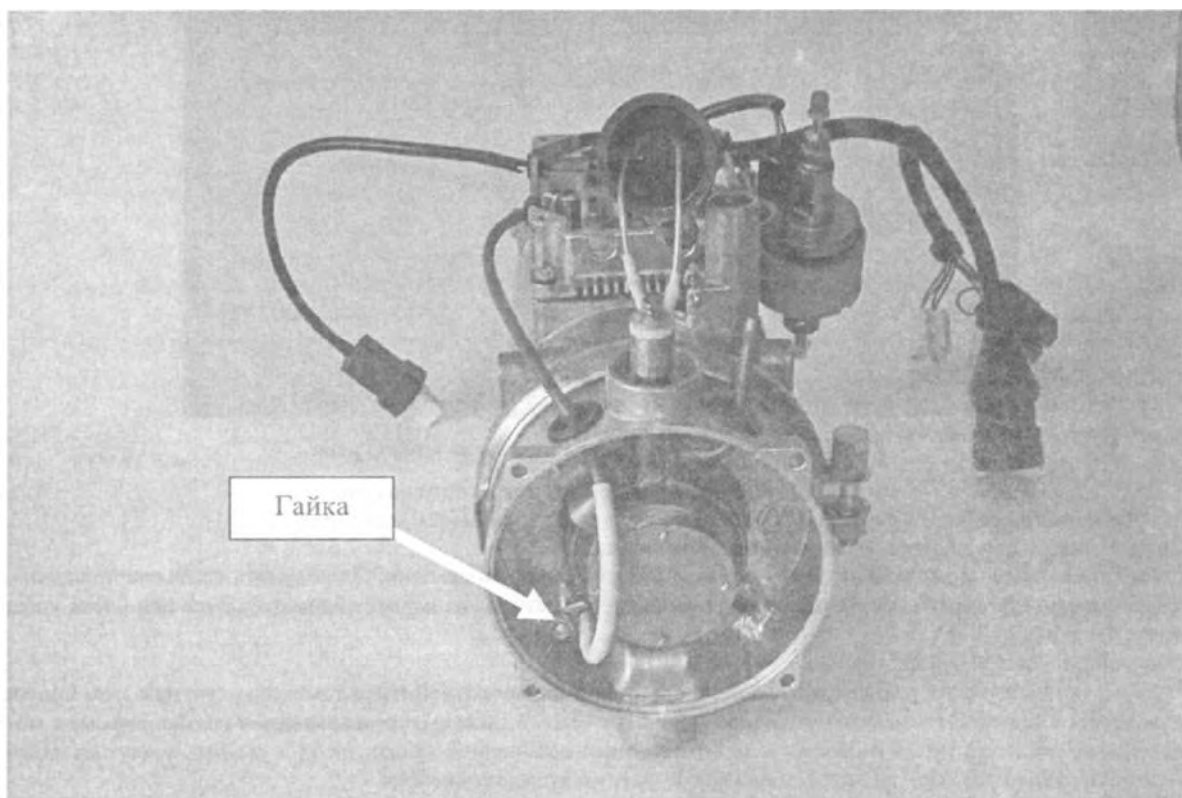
Нагреватель со снятым нагнетателем воздуха для замены индикатора пламени
